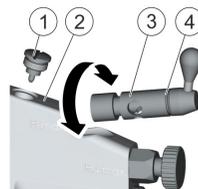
O-Ring an der Flachstrahlregulierung tauschen
